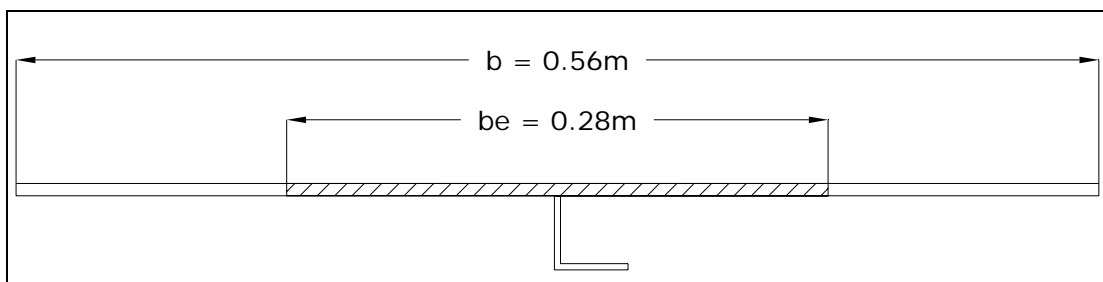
Ancho efectivo calculado para el refuerzo longitudinal de fondo
